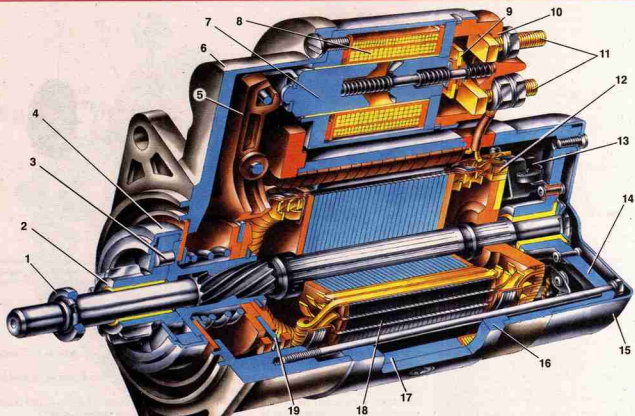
Стартер 29.3708: 1 – ограничительное кольцо; 2 – шестерня привода; 3 – ролик обгонной муфты; 4 – обгонная муфта; 5 – рычаг привода; 6 – крышка со стороны привода; 7 – якорь реле; 8 – обмотка реле; 9 – контактная пластина; 10 – крышка реле; 11 – контактные болты; 12 – коллектор; 13 – щетки; 14 – крышка со стороны коллектора; 15 – кожух; 16 – корпус; 17 – полюс статора; 18 – якорь; 19 – поводковое кольцо
